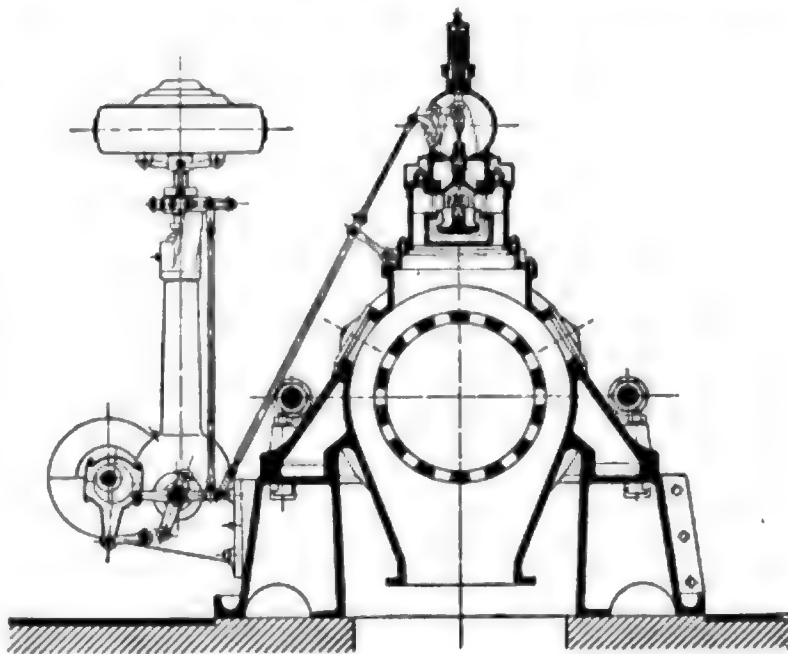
Zwangläufig gesteuertes Rücklaufventil, Patent König der Ascherslebener Maschinenbau-Aktiengesellschaft.
